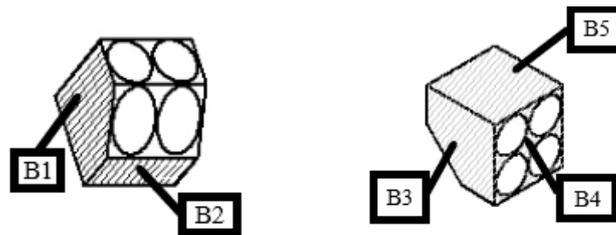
Posisi Pengukuran Presisi Dimensi Objek Kompleks
